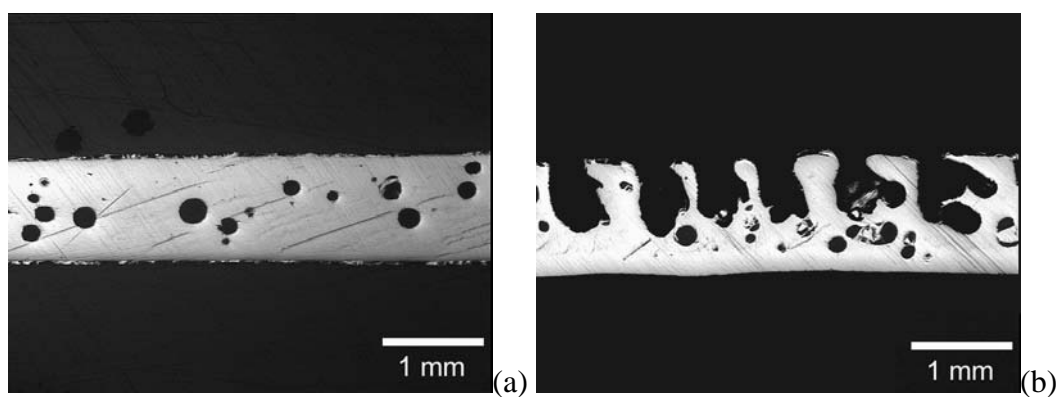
Defeitos em soldagem. (a) porosidade interna e (b) furos.
